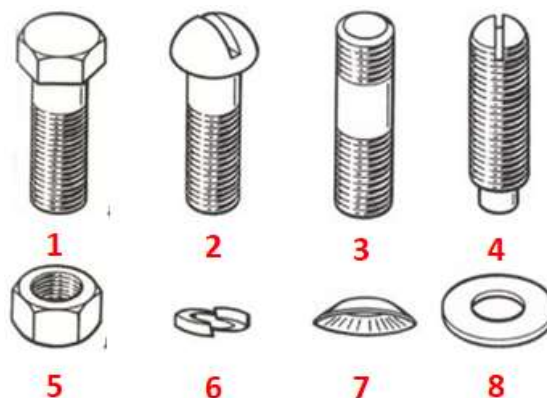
Соединительные детали для резьбовых соединений: 1 – болт, 2 – винт, 3 – шпилька, 4 – установочный винт, 5 – гайка, 6 – пружинная шайба, 7 – деформируемая шайба, 8 – плоская шайба
